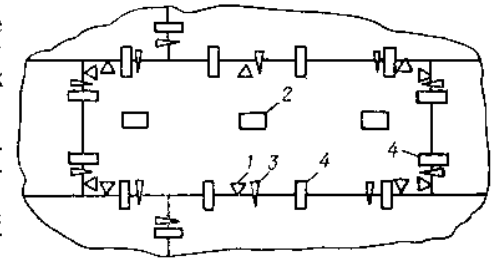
Схема размещения сборочных приспособлений на негабаритном элементе.
